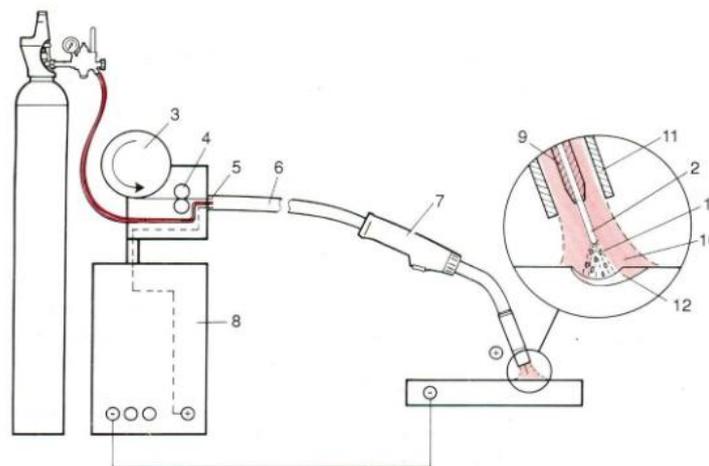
Partes de proceso MIG/MAG. Fuente: [21]
